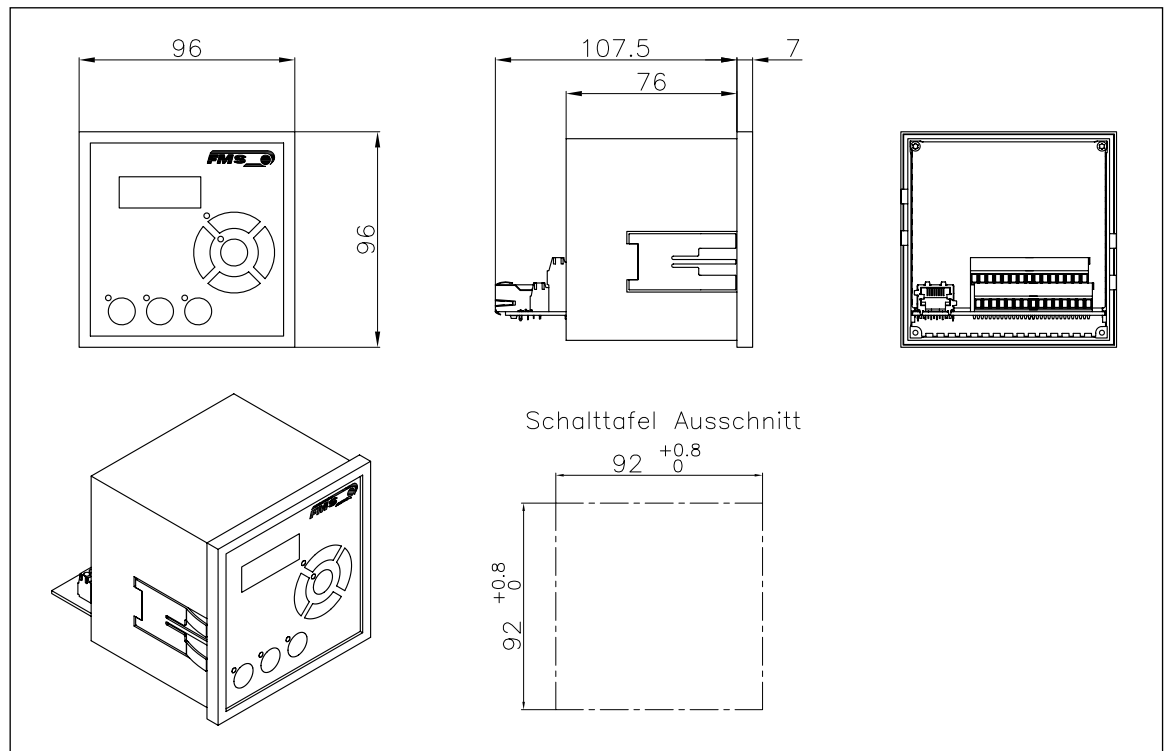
CMGZ309.S Gehäuse für Schalttafelmontage (RJ-45 Stecker)
